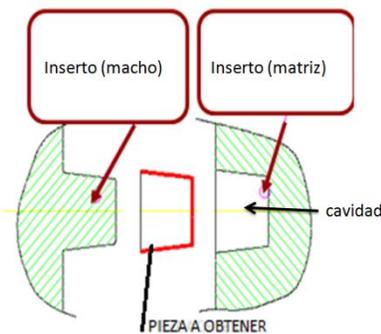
Ejemplo de insertos hembra, macho y la pieza a obtener[12]
